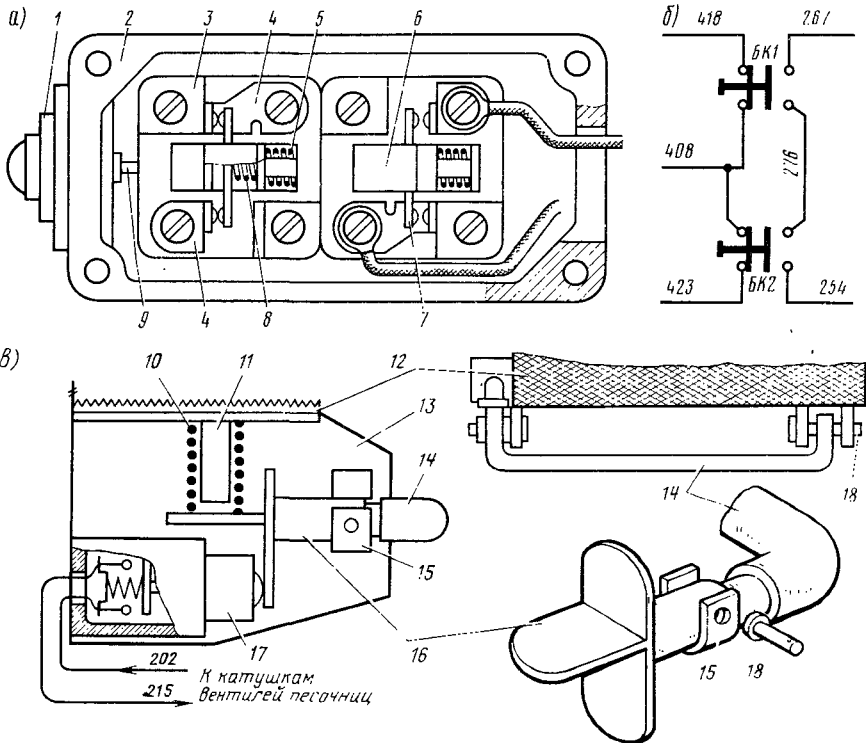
Блокировочное устройство дверей (а), схема его электрических соединений (б) и рычажный привод песочницы (в):
